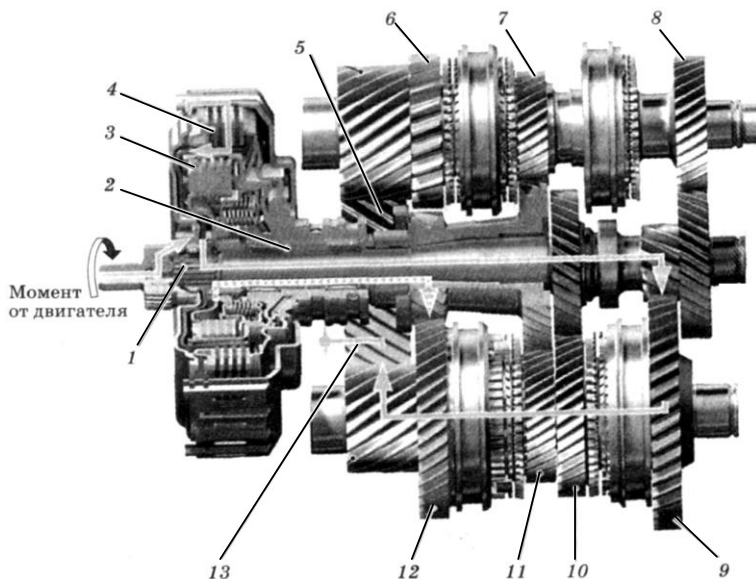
Схема коробки передач с двойным сцеплением (работа на первой передаче):
